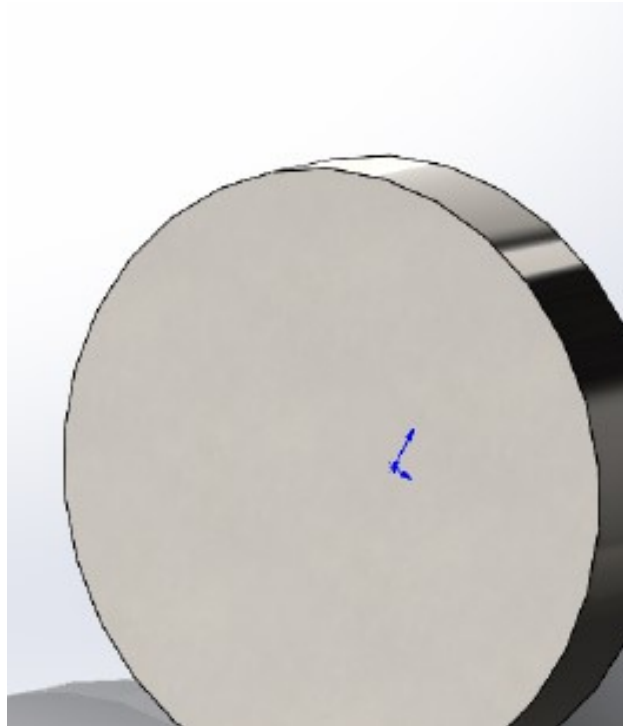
Ескіз заготовки (круглий прокат)
